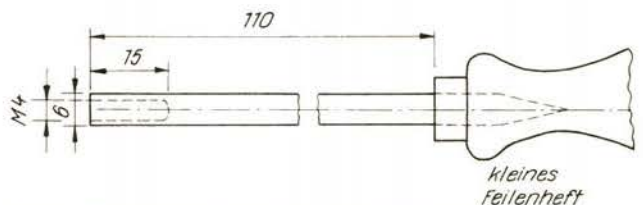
Werkzeug für den Lagerzapfen des Zahnrads B 11
